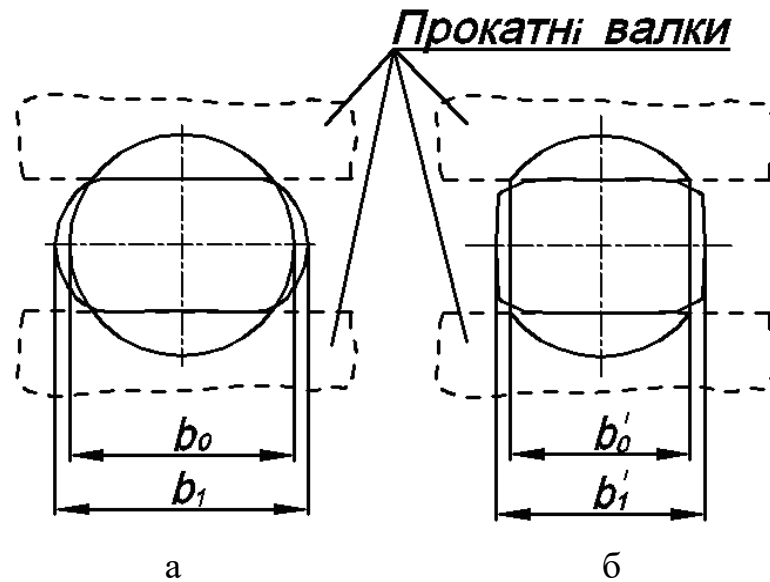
Схеми поперечних перерізів за прокатування циліндричних заготовок в гладких валках: з ПЗ (а) та без ПЗ (б)
